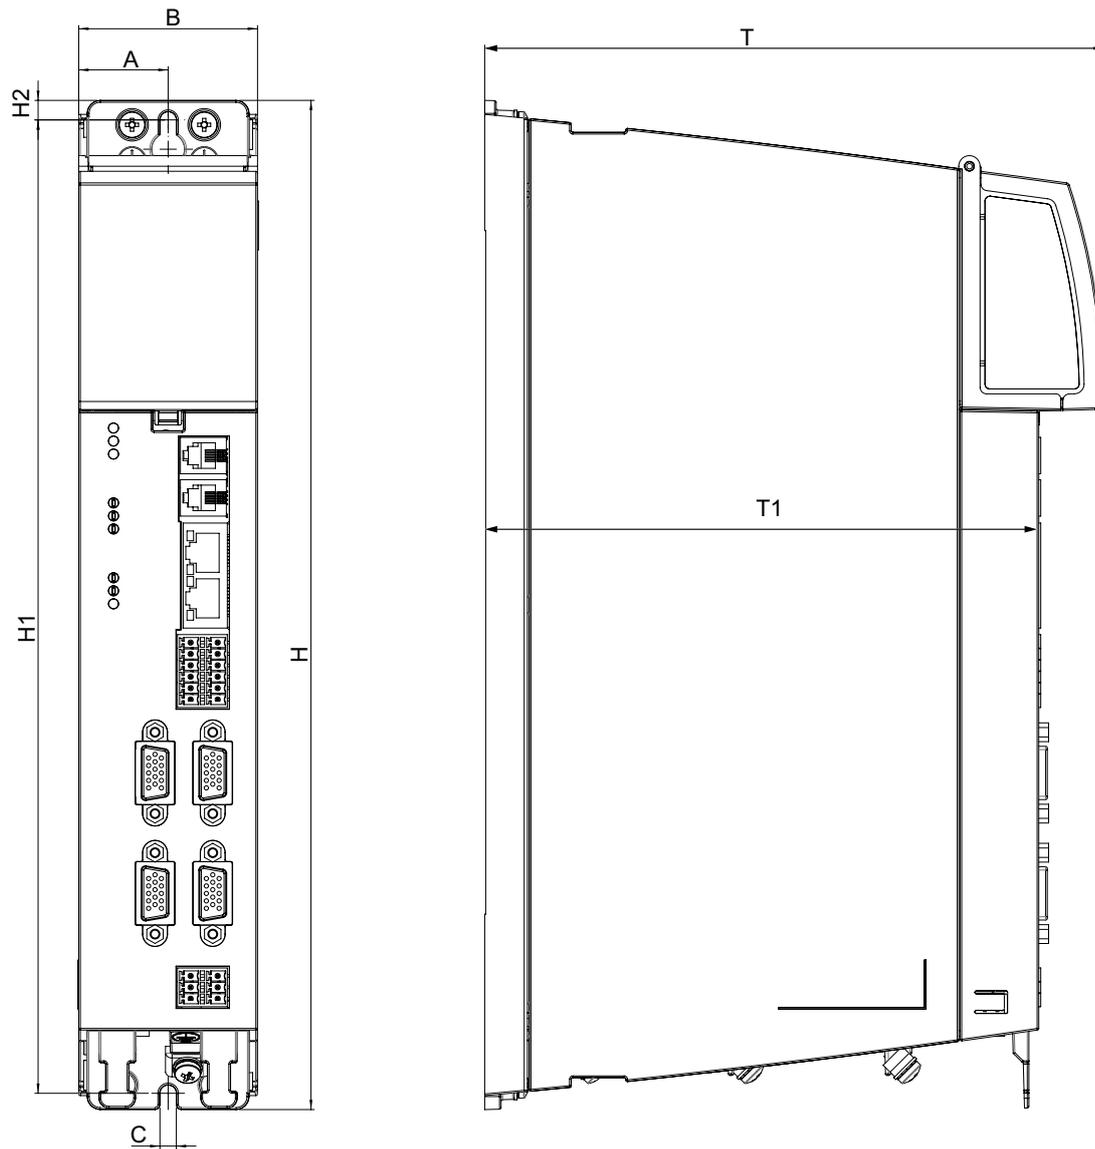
Maßzeichnung JM-3000 Servoverstärker BG1 Cold Plate (Maße siehe Tabelle 2.2)
